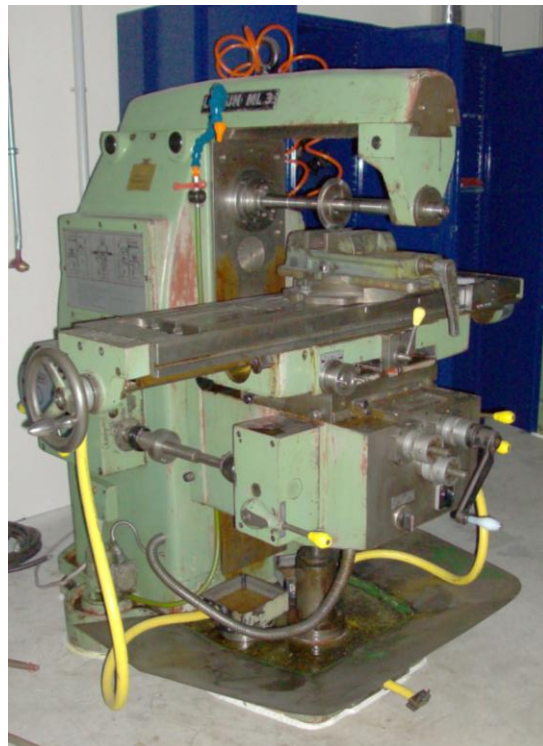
Detailaufnahme Probenfertigung
